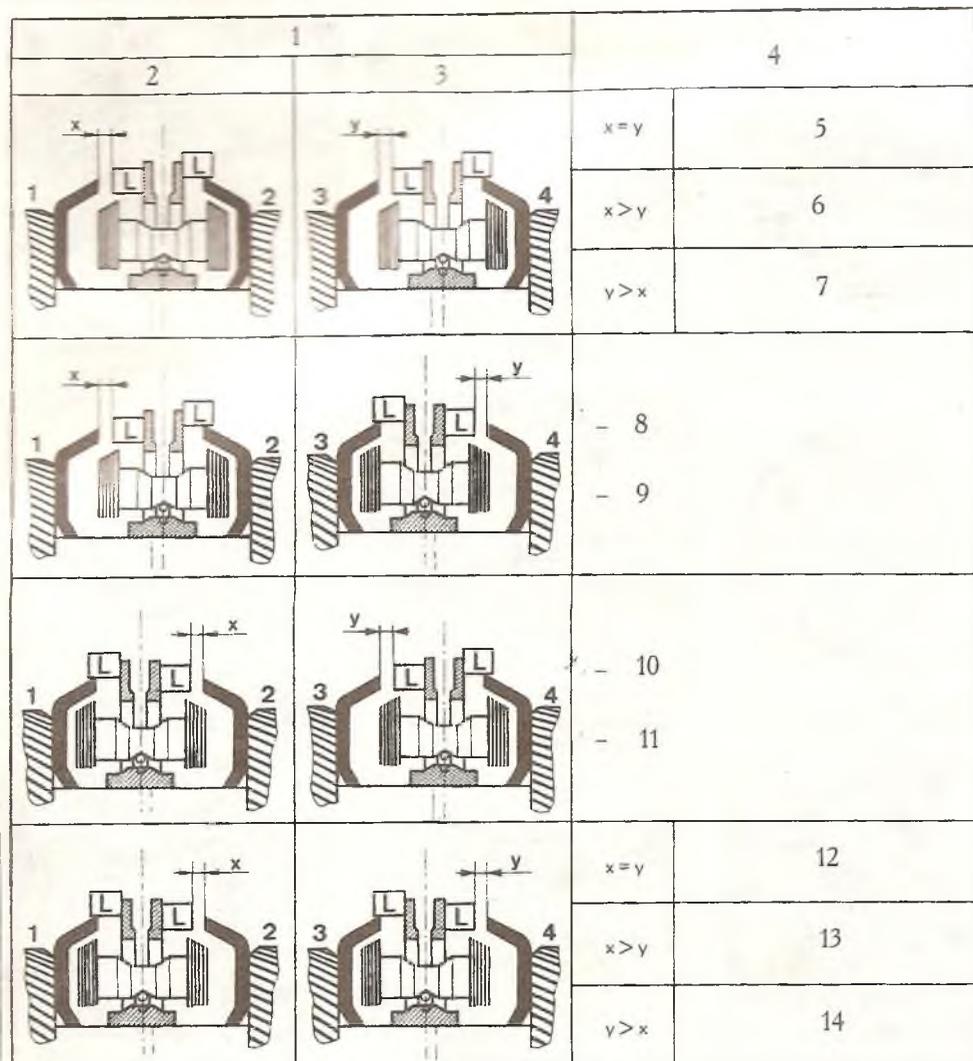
Исправление плохой центровки обоих синхронизаторов (обозначение величин см. на рис. 6.8) (раздел 3):
